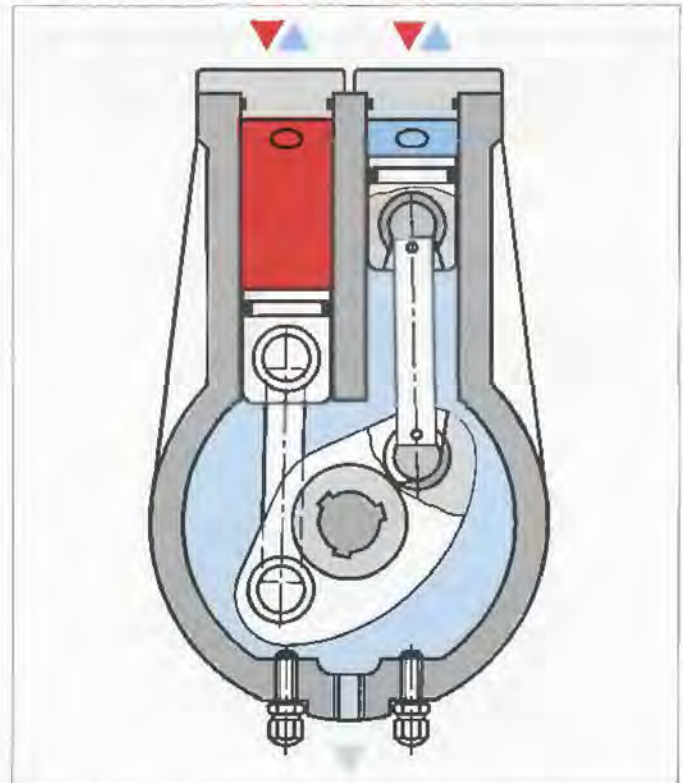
Поворотный гидродвигатель с параллельно работающими поршнями
